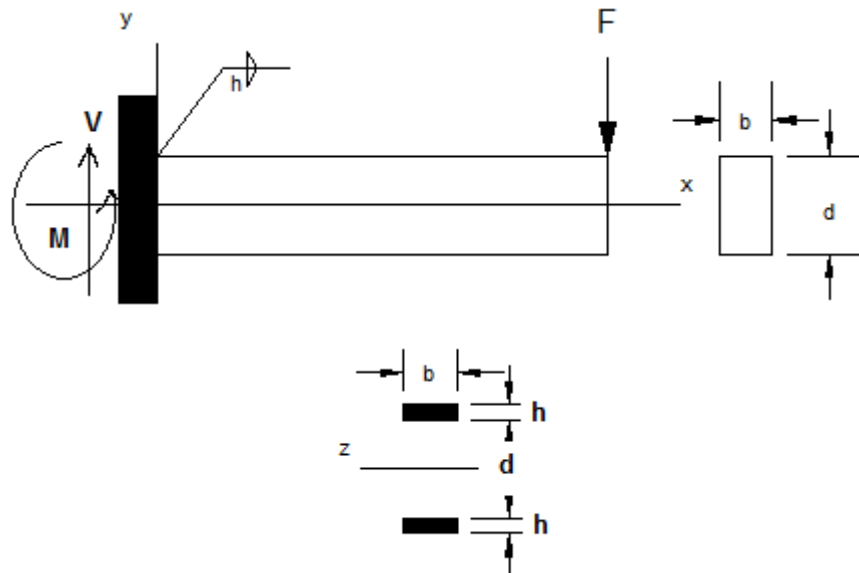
Voladizo soldado en extremos y sometido a flexión.
